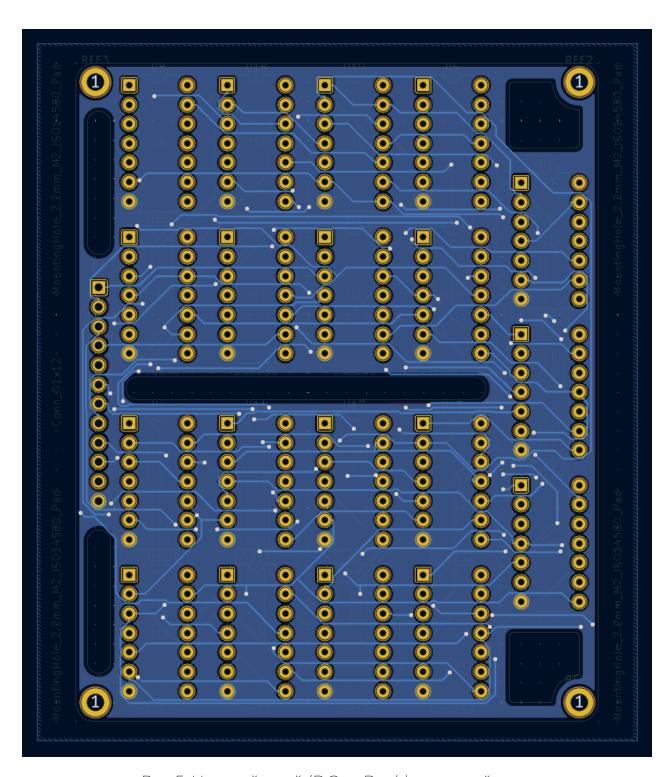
Нижний слой (B.Cu - Back) печатной платы
